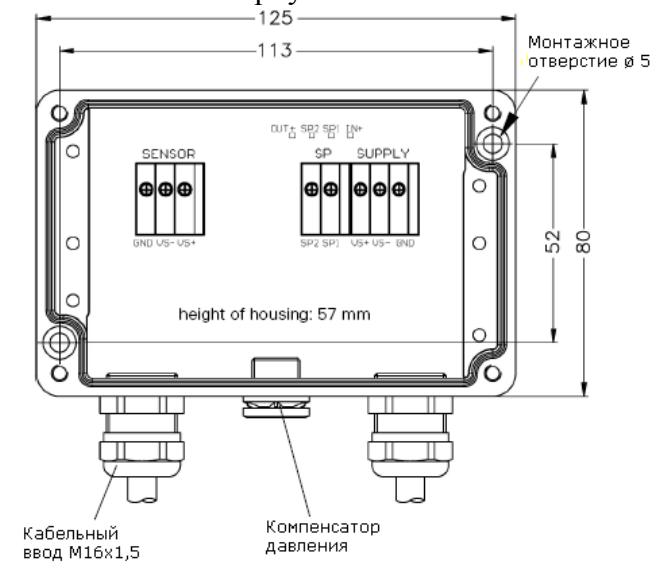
Габаритные и присоединительные размеры индикатора.
